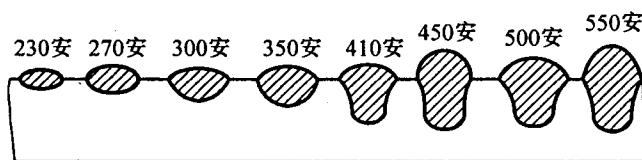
焊接电流对焊缝成形的影响
